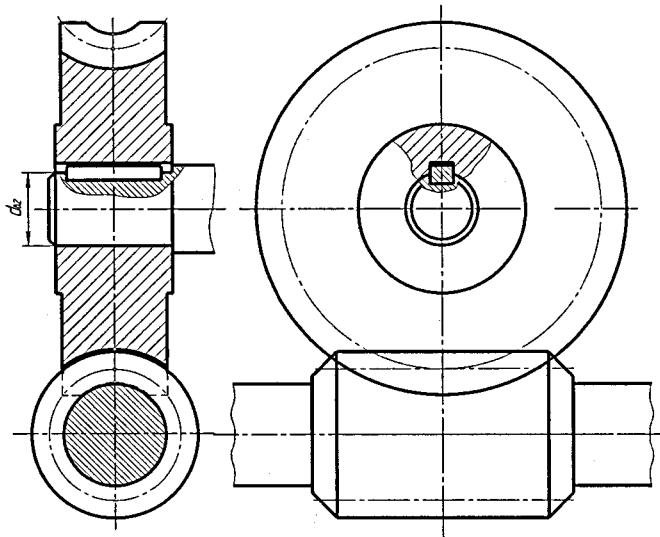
Графічна умова до викреслювання черв'ячної передачі
